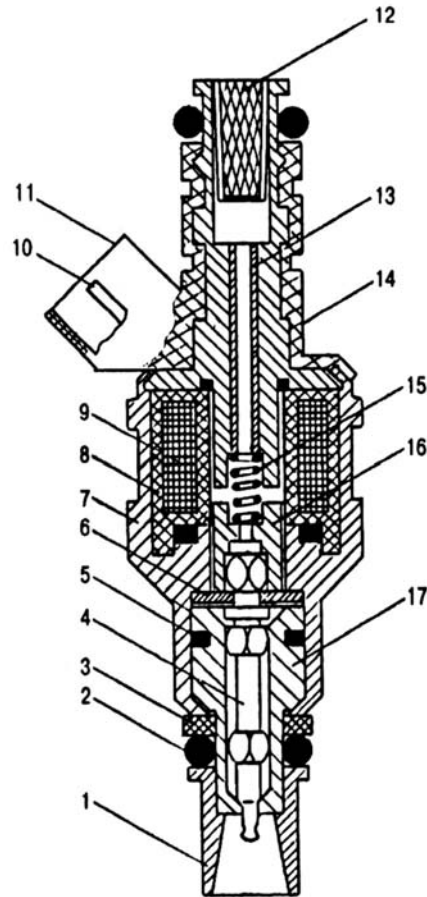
Электромагнитная форсунка: 1 - насадка распылителя; 2 - уплотнительное кольцо; 3 - шайба; 4 - игла клапана; 5 - уплотнитель; 6 - ограничительная шайба; 7 - корпус; 8 - изолятор; 9 - обмотка электромагнита; 10 - штекер; 11 - колодка; 12 - фильтр; 13 - трубка; 14 - крышка; 15 - пружина; 16 - сердечник электромагнита; 17 - корпус клапана-распылителя
